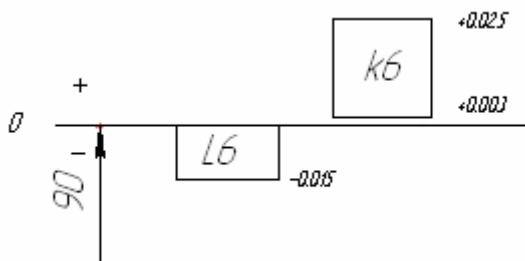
Схема расположения полей допуска посадки внутреннего кольца
